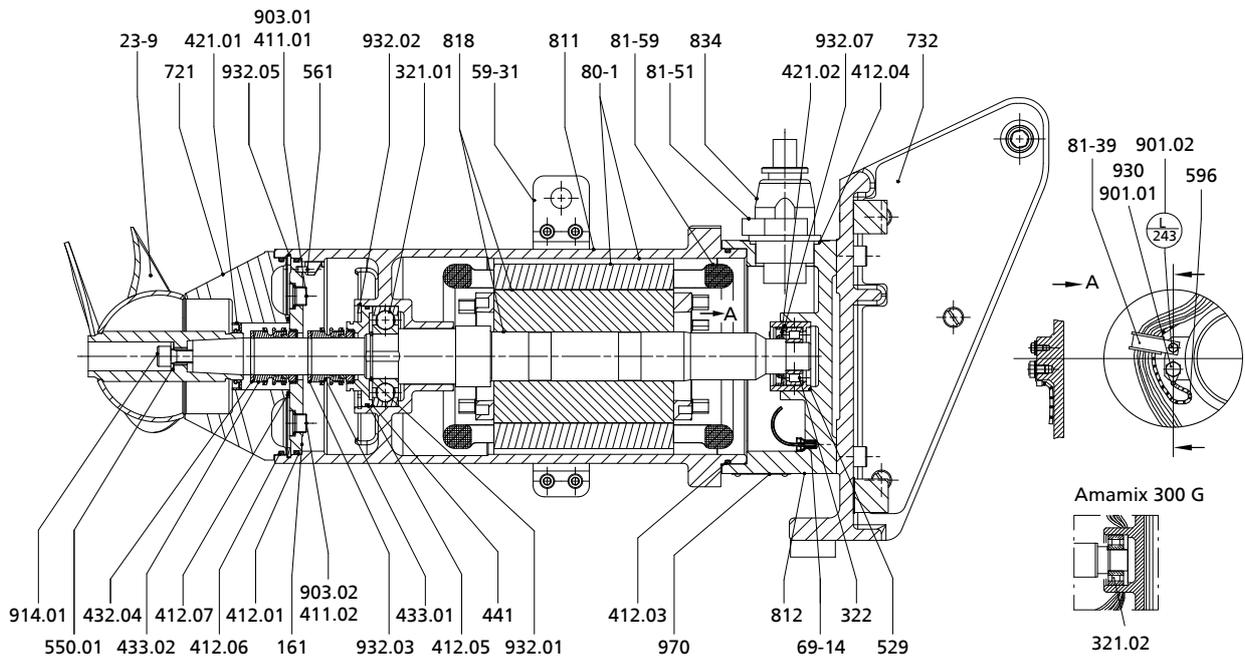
Gesamtzeichnung Amamix 300/400/600, Motorgehäusewerkstoff Grauguss
